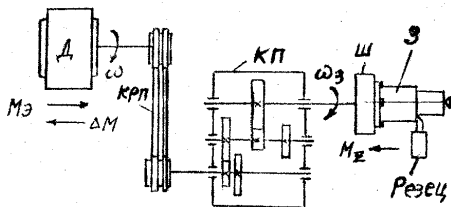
Кинематическая схема ЭП шпинделя токарного станка
